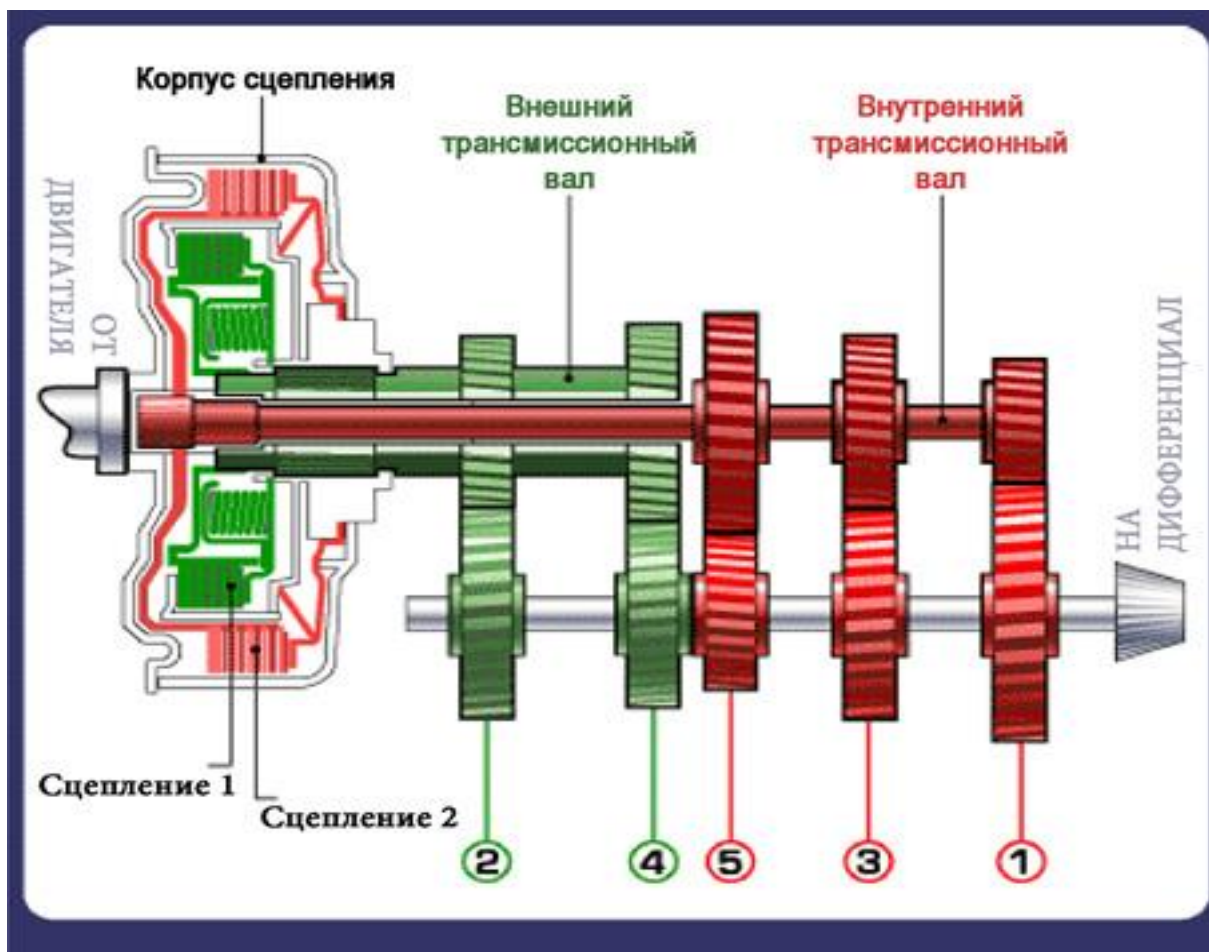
Схема роботизированной КПП с двойным сцеплением
